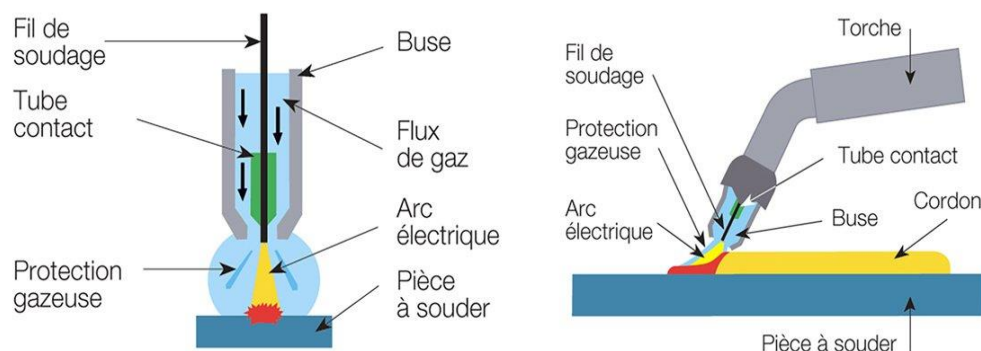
Principe soudage MIG MAG [1]
